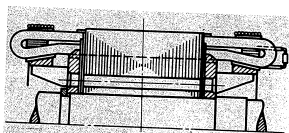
Крепление сердечника ротора на валу и крепление обмотки ротора
